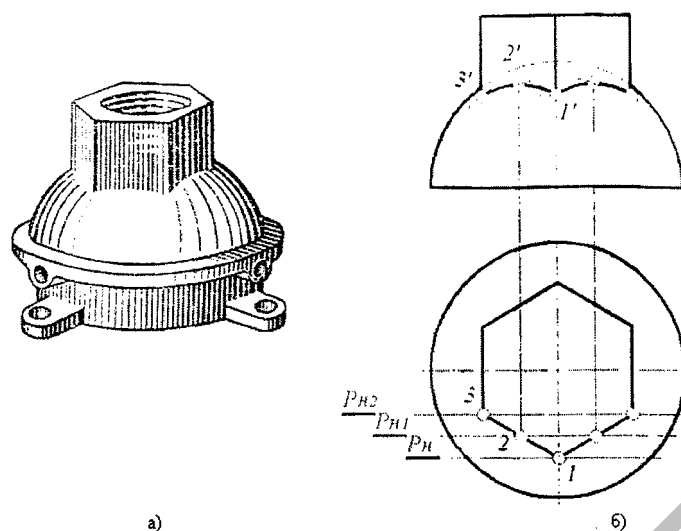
Пересечение сферической и призматической поверхностей:
